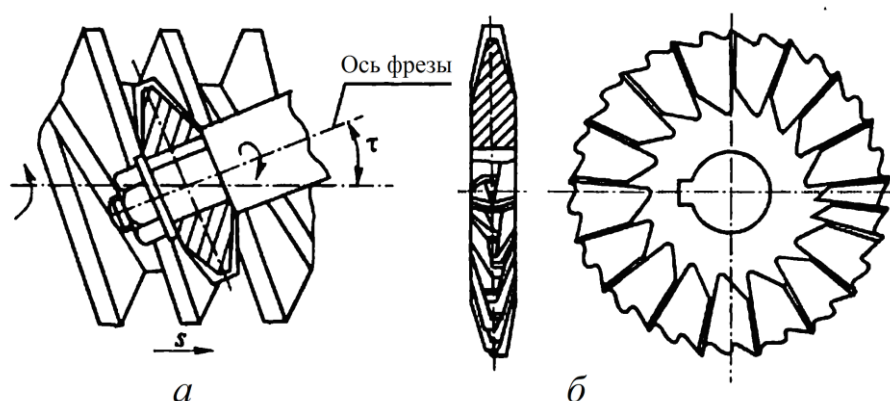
Дисковые фрезы: а – схема установки фрезы относительно заготовки; б – фреза для нарезания трапецеидальной резьбы
